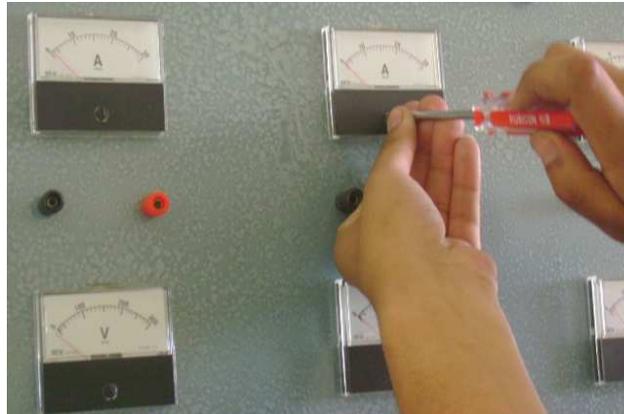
Colocación de Voltímetros y Amperímetros (Parte frontal)
